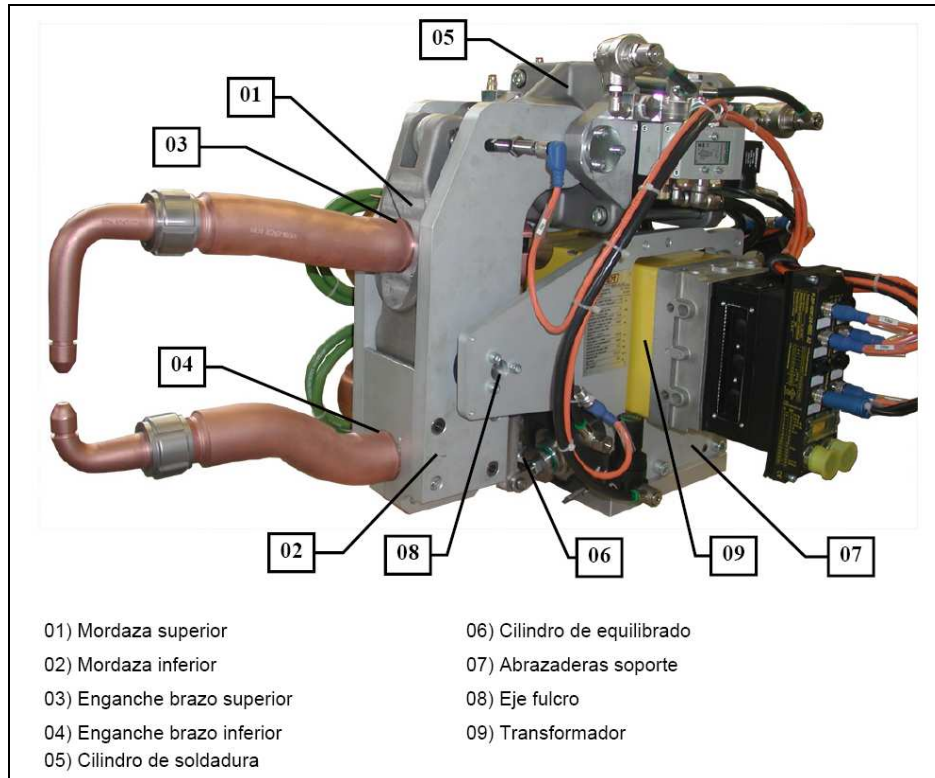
Elementos básicos de una pinza de soldadura
